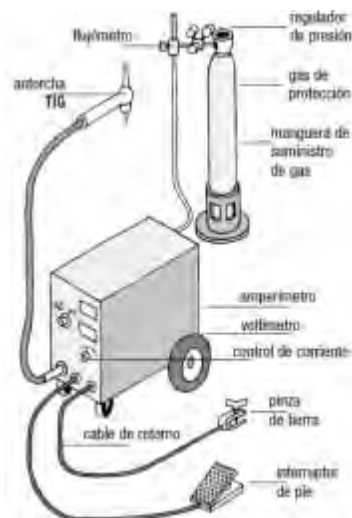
Dispositivos soldadura TIG.
